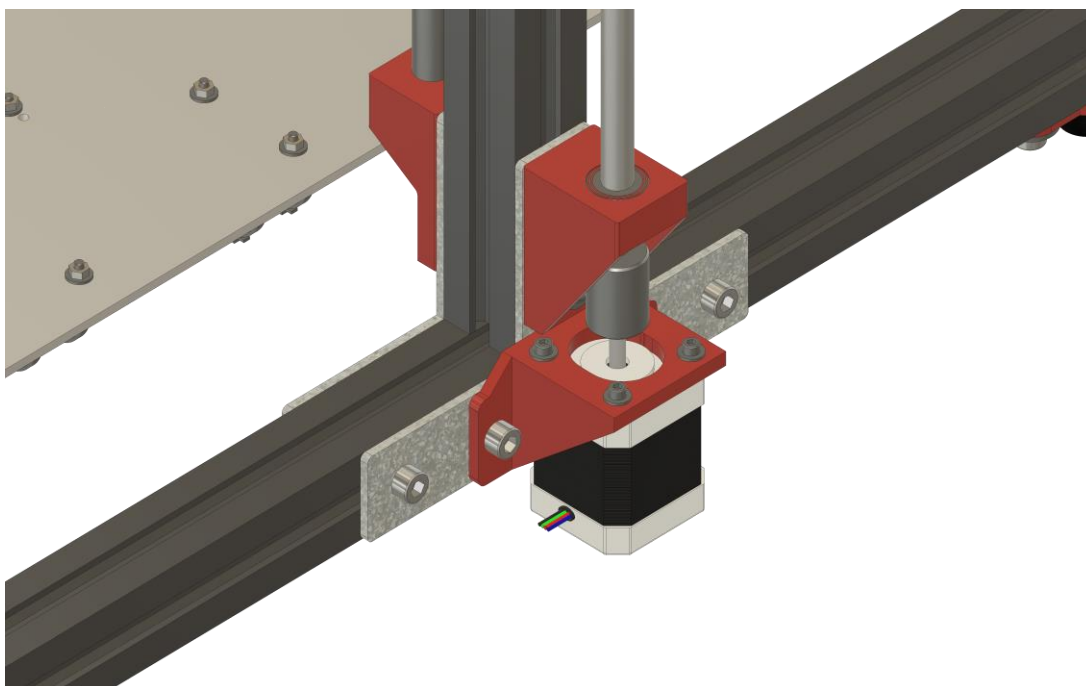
Komponenty pro sestavení krokových motorů osy Z
